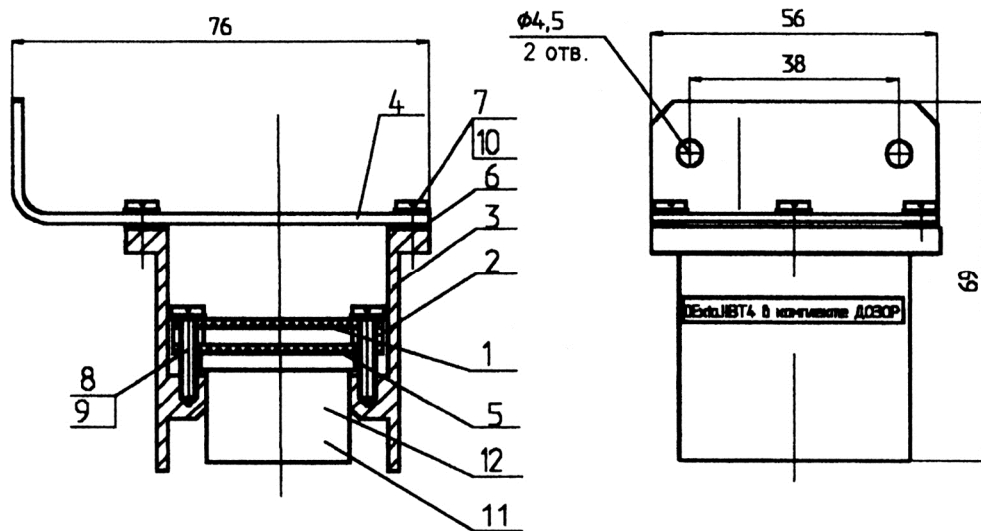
Конструкція та габаритні розміри електрохімічного датчика SENS: 1 – плата датчика; 2 – стійка; 3 – корпус; 4 – кронштейн; 5 – прокладка; 6 – шайба; 7, 8 – гвинт; 9, 10 – шайба; 11 – розетка ОНЦ-РГ-09-4/14-Р1; 12 – чутливий елемент “SensorE” з дифузійним вікном.
